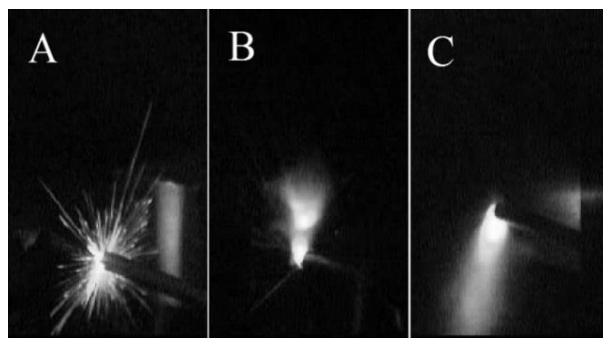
Плазменный шнур в зазоре постоянного магнита: А – поджиг электрической дуги; В, С – сила Ампера отклоняет плазмоид вверх и вниз при смене полюсов магнита или направления сварочного тока
